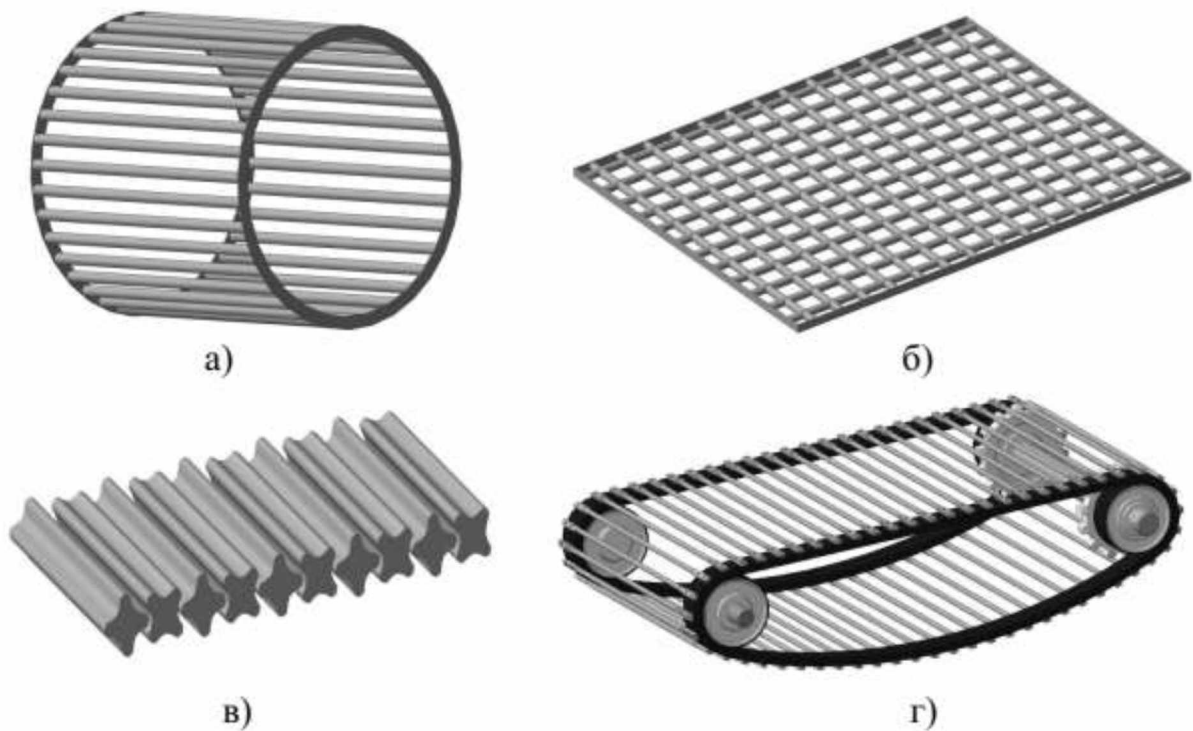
Основні типи сепаруючих робочих органів: а) барабанний грохот; б) решітний грохот; в) валковий грохот; г) прутковий елеватор
